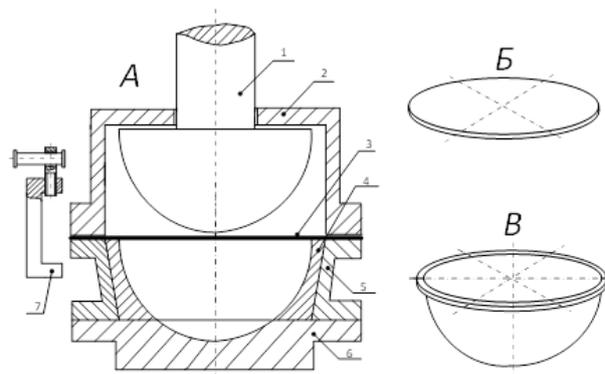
Принципиальная схема конструкции штамповой оснастки для штамповки полушфер: А — конструкция штамповой оснастки для формирования полушфер, Б — вид заготовки для штампования, В — вид готовой продукции (полушферы для изготовления емкостей); 1 — пуансон, 2 — верхняя крышка штампа, 3 — заготовка, 4 — съемные вкладыши (4 шт.), 5 — корпус штампа, 6 — основание штампа, 7 — струбцины для скрепления частей штамповой оснастки (8 шт.)
